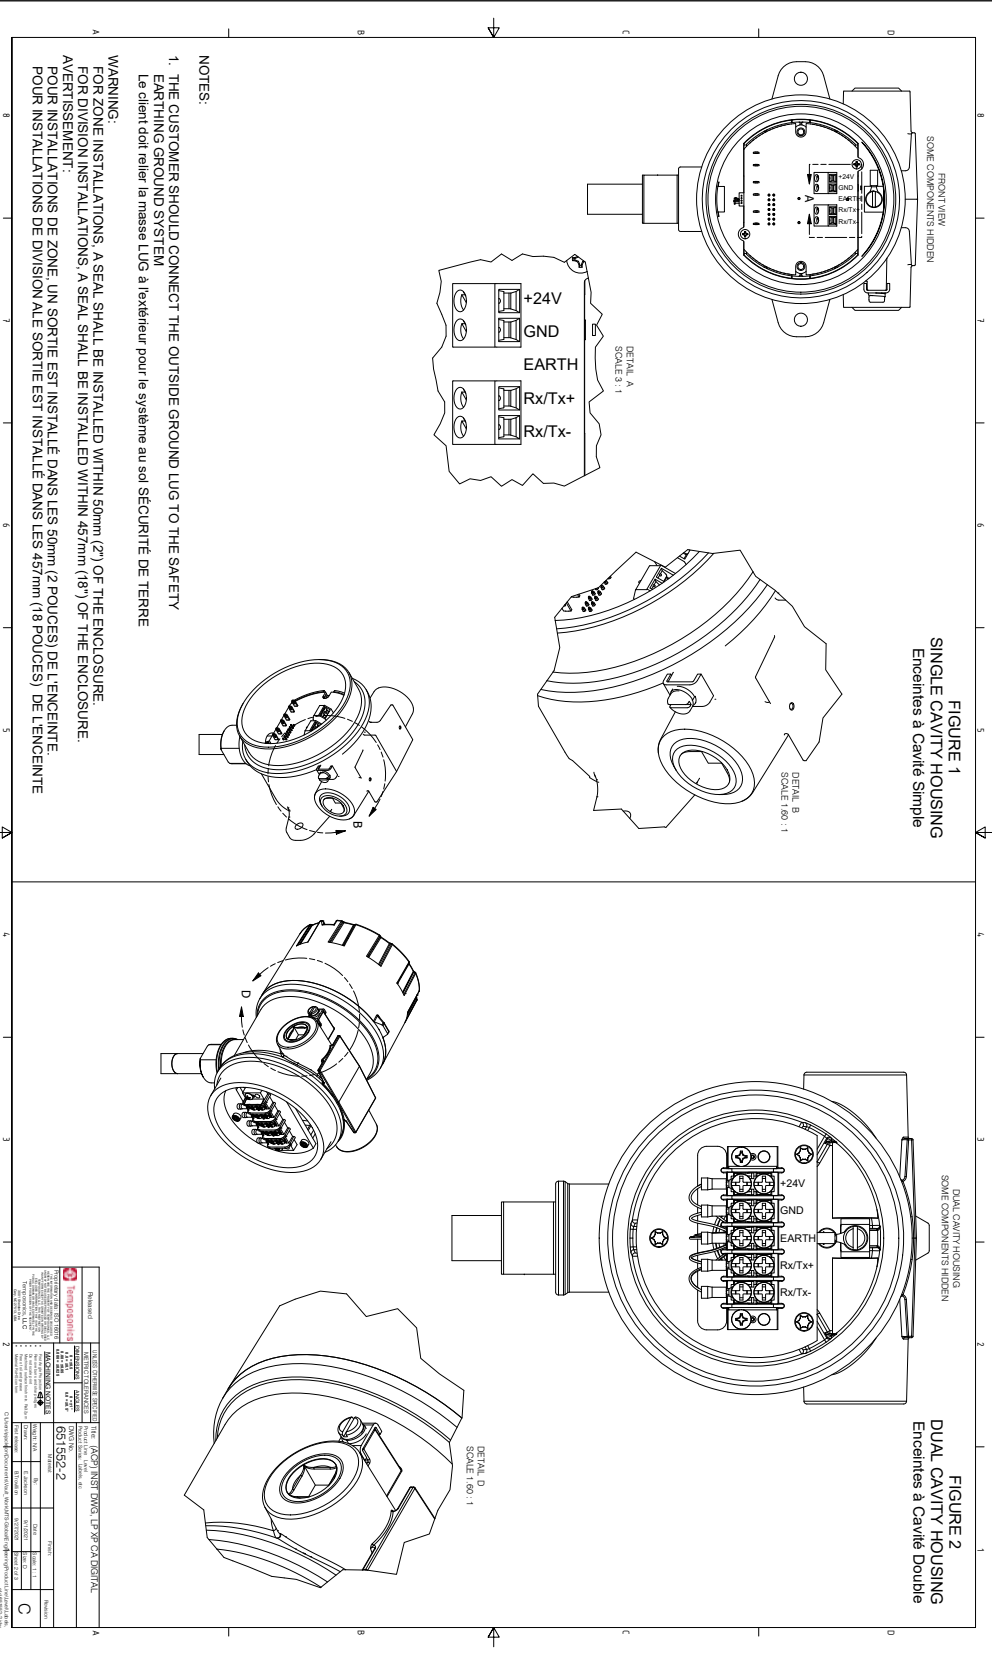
Explosionsschutz, FMC-Montagezeichnung, Modbus und DDA, Seite 2
